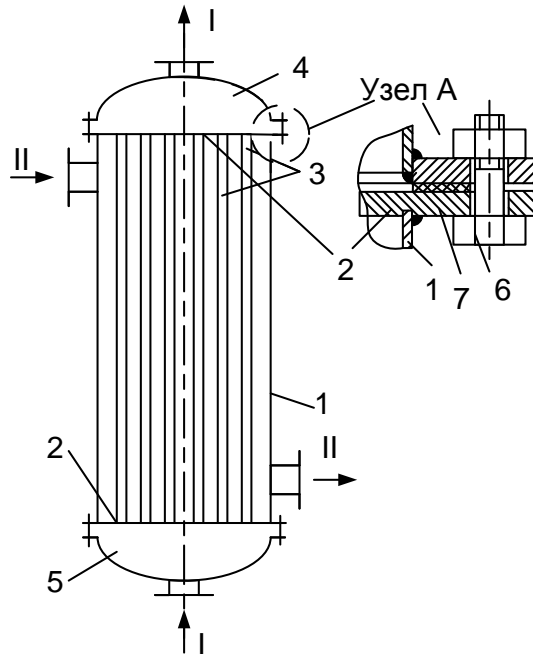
Кожухотрубчатый теплообменник жесткой конструкции:
